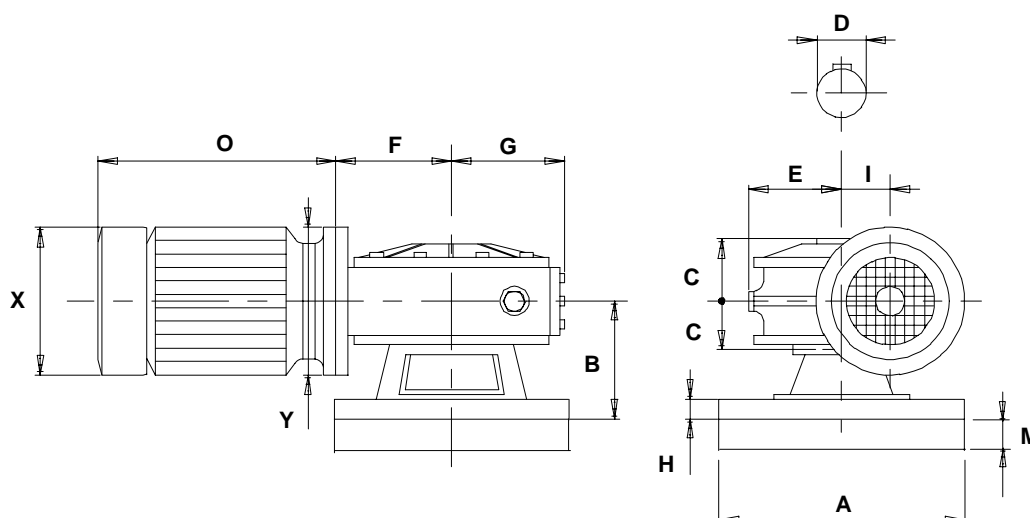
Motoréducteur STM "RMI" - Version à bride.
